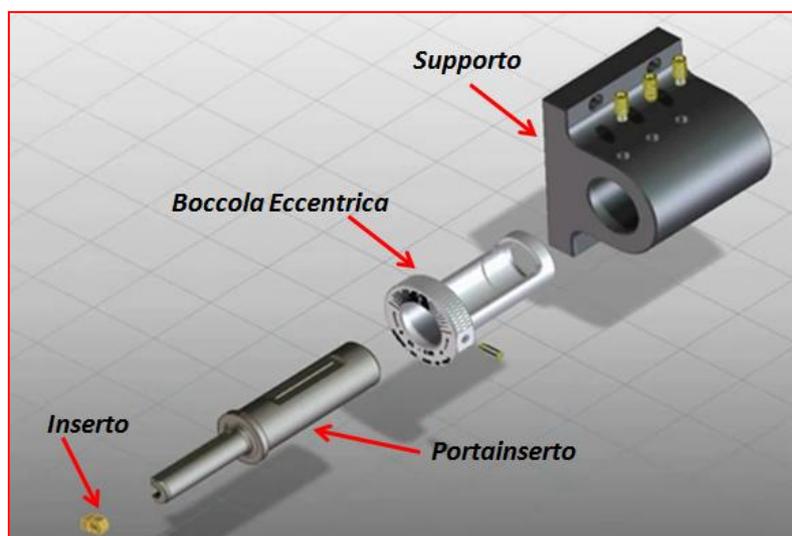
Composizione di un sistema di brocciatura REV BROACHING TOOL
